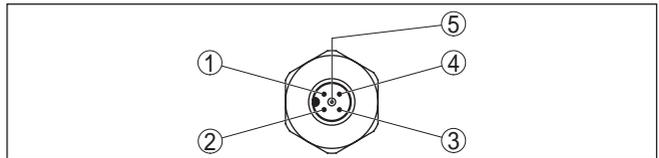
Sicht auf den Steckverbinder (M12 x 1-Stecker - 5-polig)
